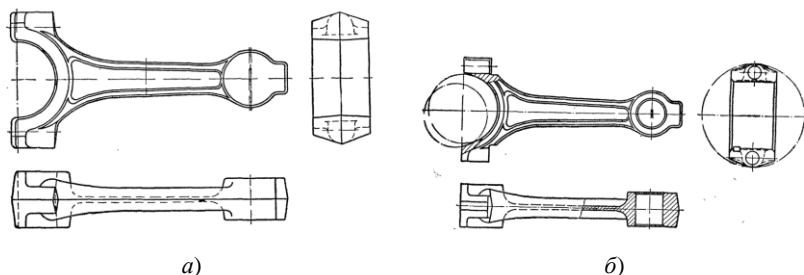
Штампованная заготовка шатуна (а), готовый шатун (б)
